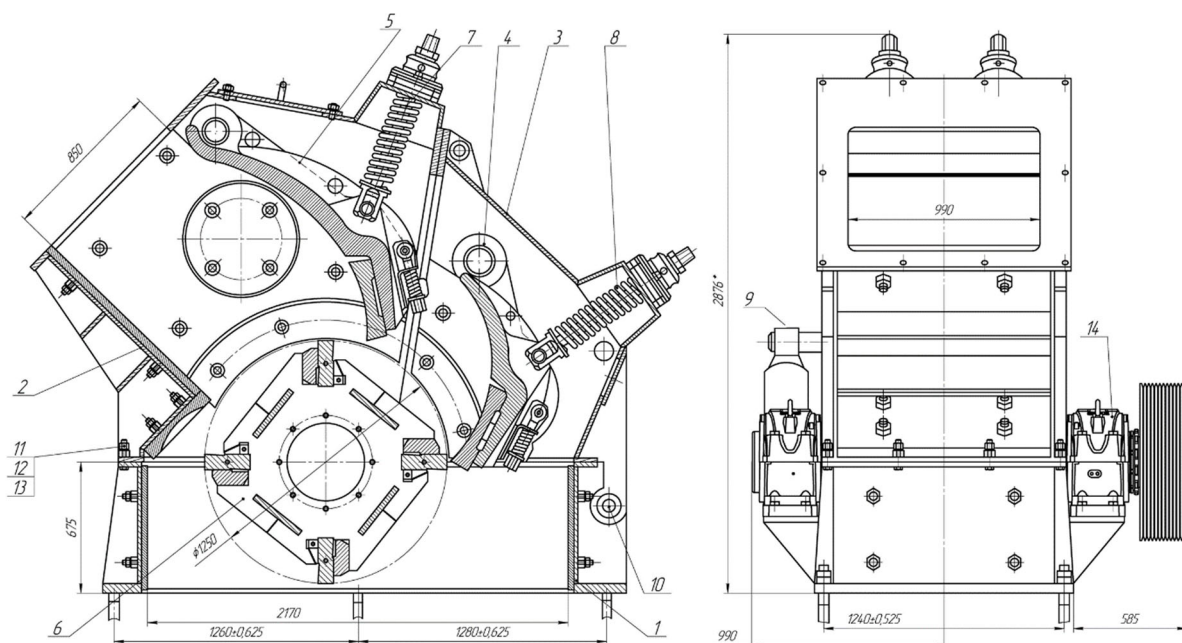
Роторна дробарка СМД-86 із запропонованою конструкцією модернізованого ротора
